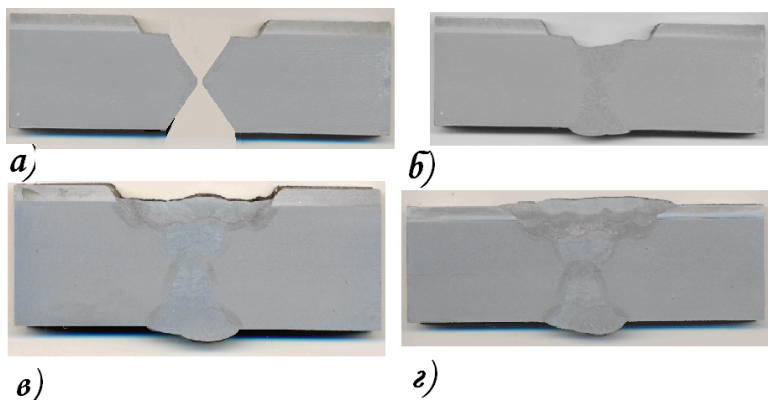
Основные этапы получения сварного соединения плакированной стали: а - разделка под сварку, тип С-37, ГОСТ 16098 – 80; б – сварка основного слоя; в – сварка переходного слоя; г – сварка плакирующего слоя
